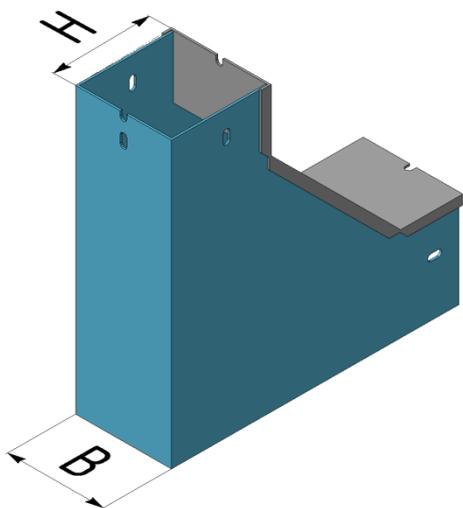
Короб угловой для поворота вверх на 90° типа КУВ. Общий вид
